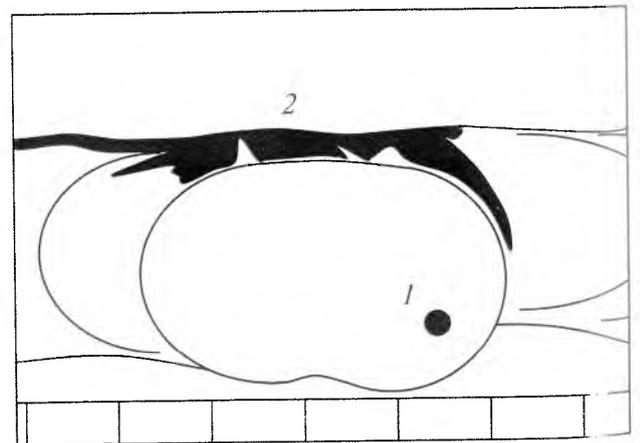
Остроугольное шлаковое включение на поверхности валика стыкового сварного соединения
